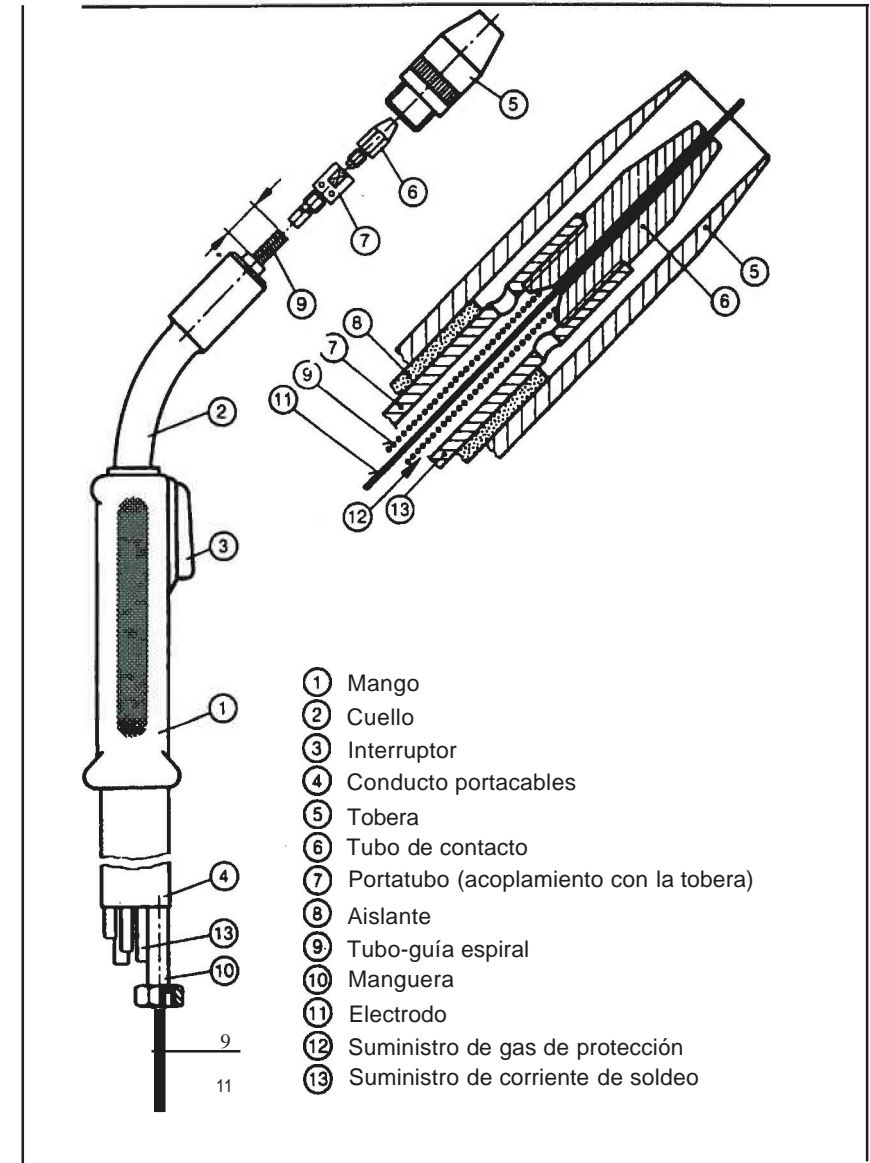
PISTOLA PARA SOLDEO MIG/MAG (ACERO AL CARBONO)
